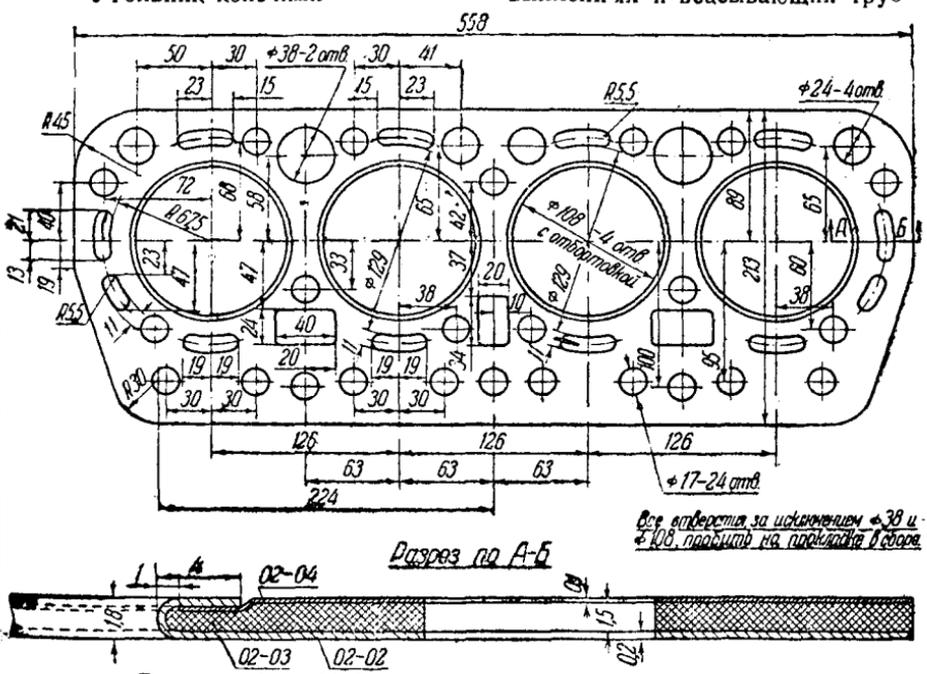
Дет. № 02к 1. Прокладка головки цилиндров
